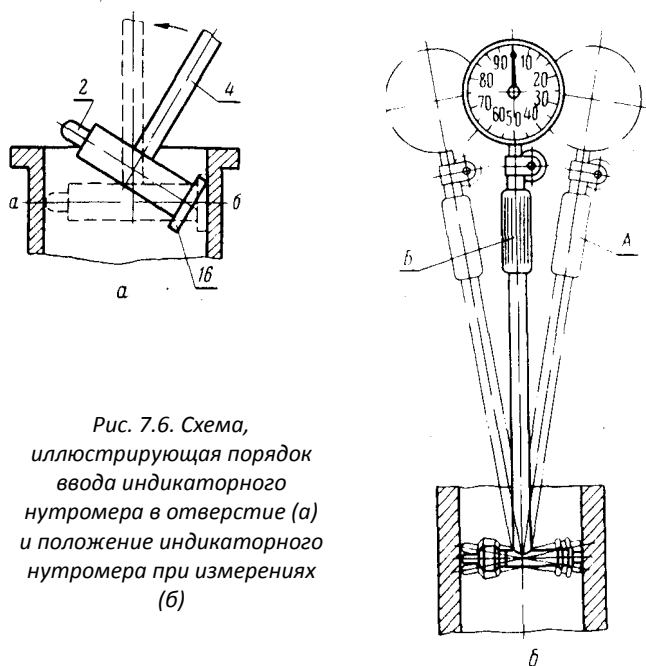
Схема, иллюстрирующая порядок ввода индикаторного нутромера в отверстие (а) и положение индикаторного нутромера при измерениях (б)
